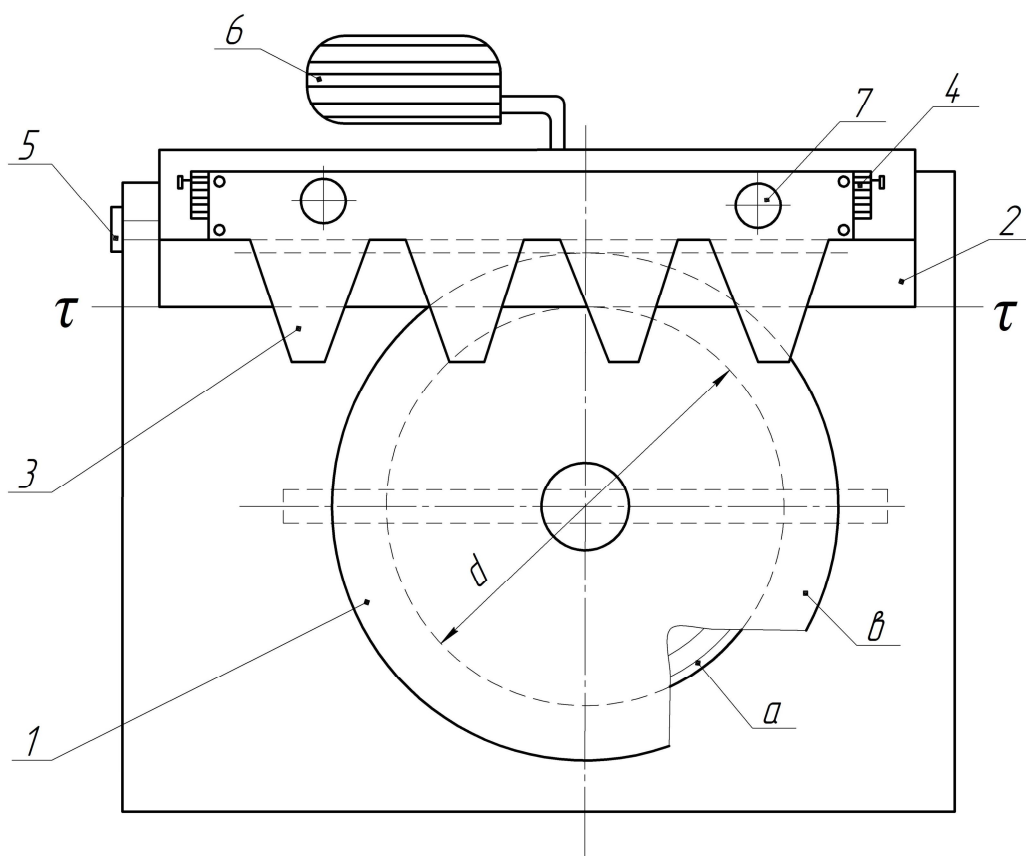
Прибор для вычерчивания профиля зубьев
